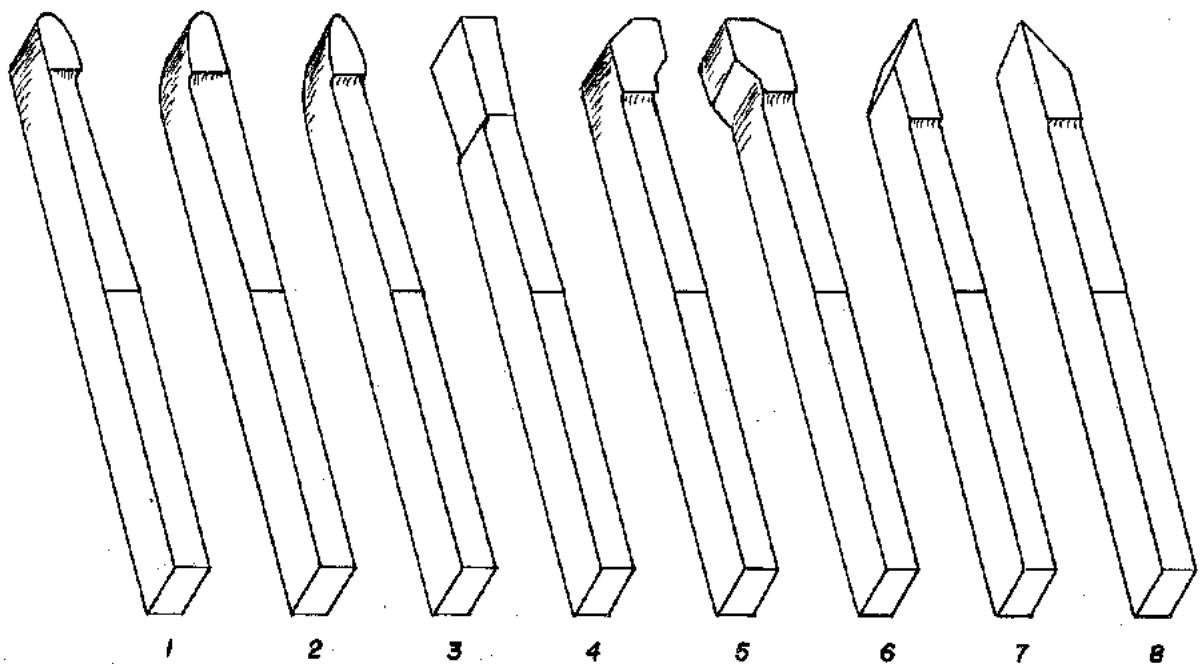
Herramientas de acepilladora, del tipo de una sola pieza.
